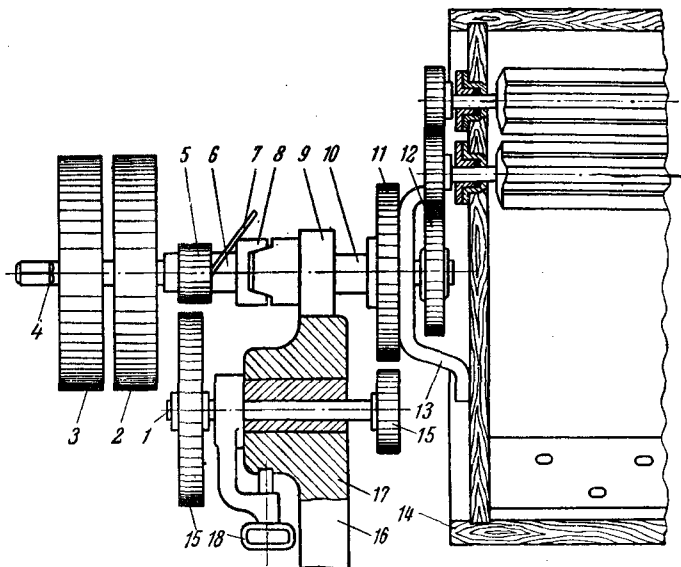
Схема приводного механизма маслоизготовителя с комбинированным приводом:
